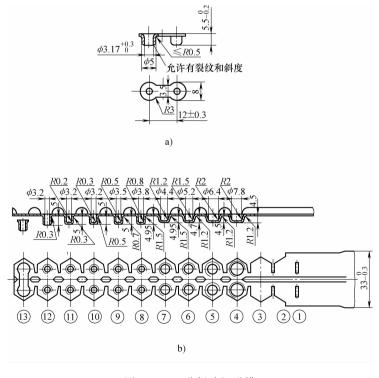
双孔焊片级进模 a) 零件图 b) 排样图
